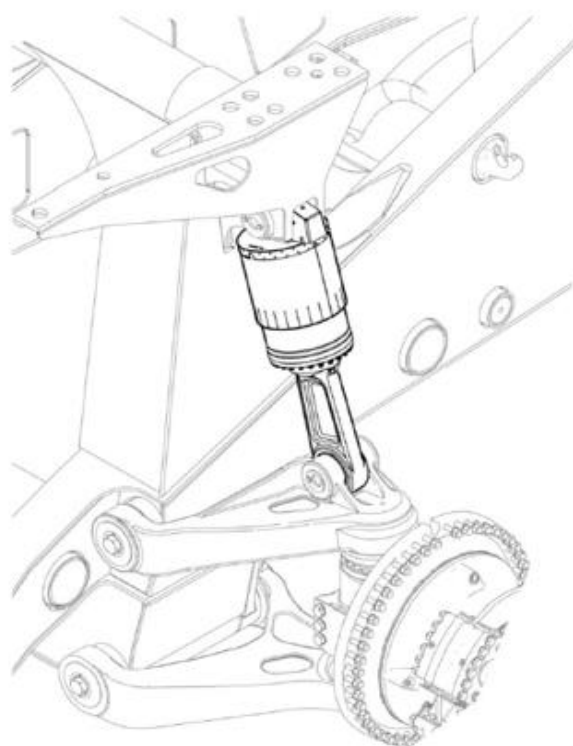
Конструкция передней подвески Liebherr T264. 1 – рама; 2 – продольный рычаг; 3 – верхняя балка; 4 – ПГР передней подвески; 5 – шкворневой механизм; 6 – ступица
